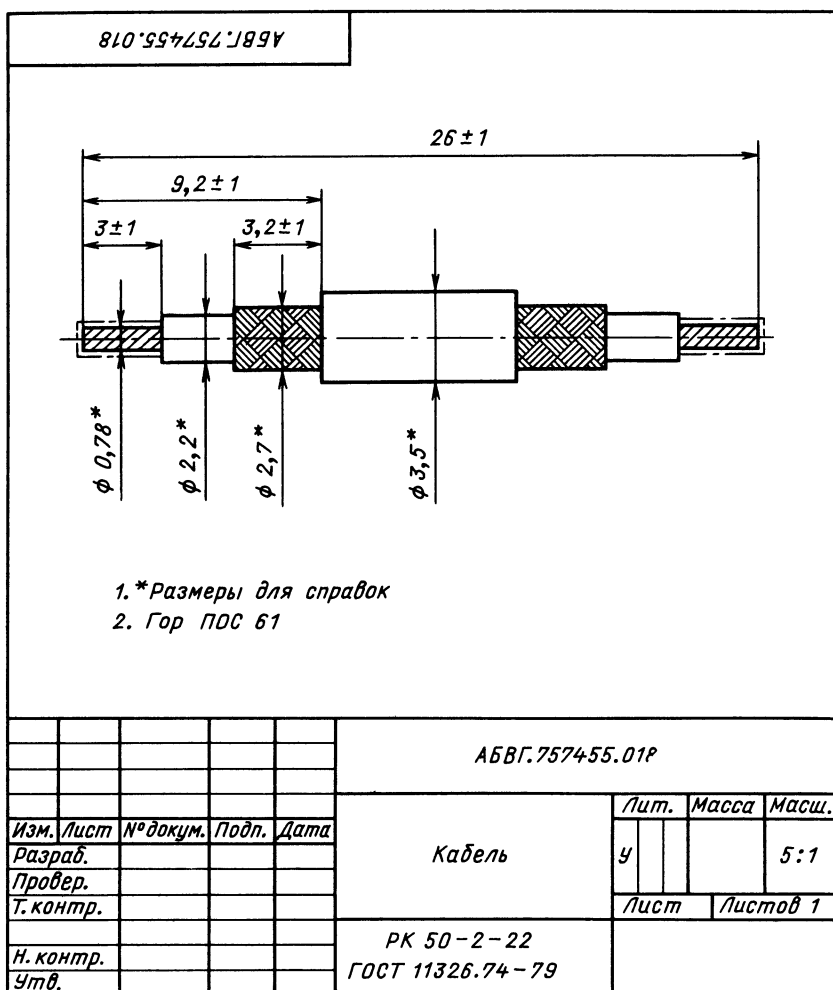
Конструкторский документ — чертеж детали «Кабель»
